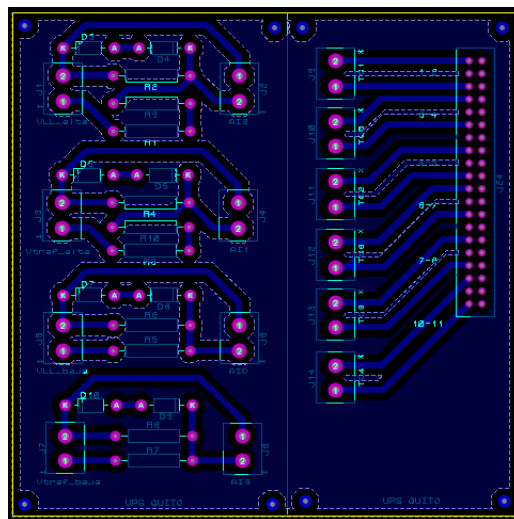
Diseño de Placas PCB para circuito de Acondicionamiento de Señal.
